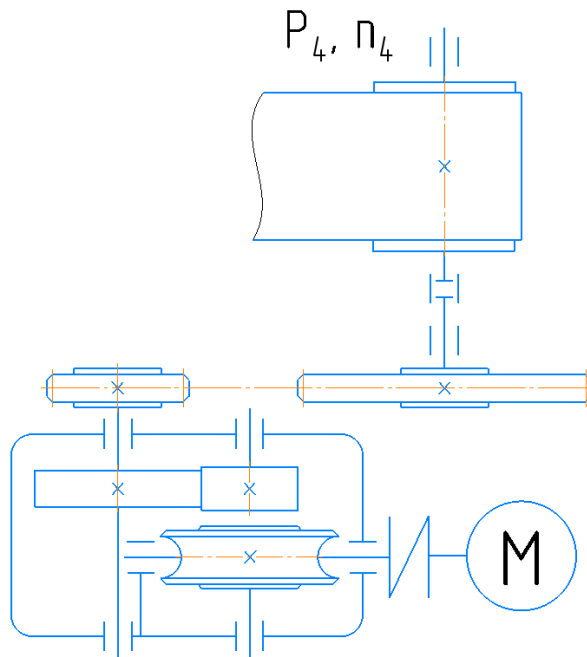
Опис кінематики триступінчастого черв'ячного редуктора, що з'єднаний з приводним барабаном.
